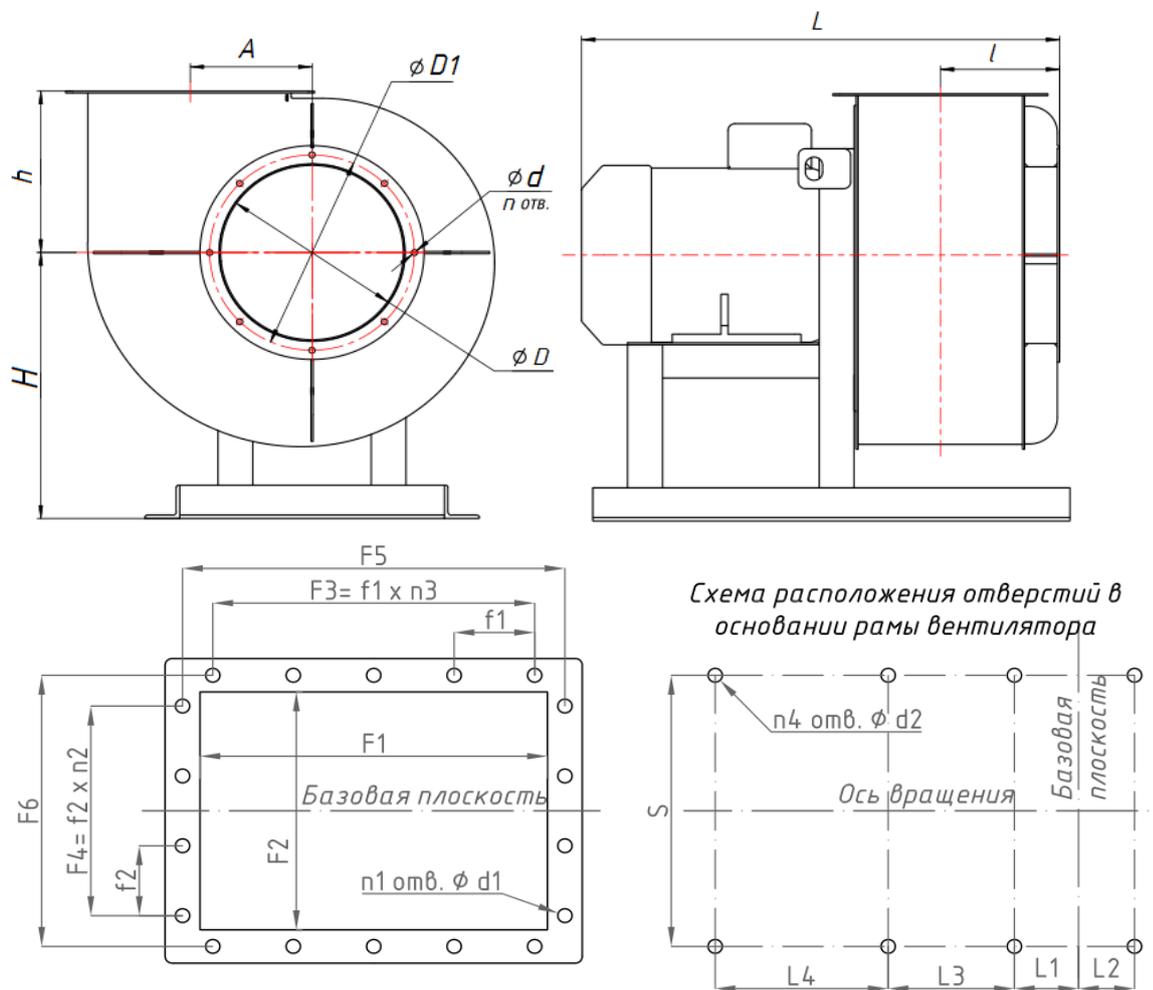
Габаритные и присоединительные размеры вентиляторов ВЦП 7-40
